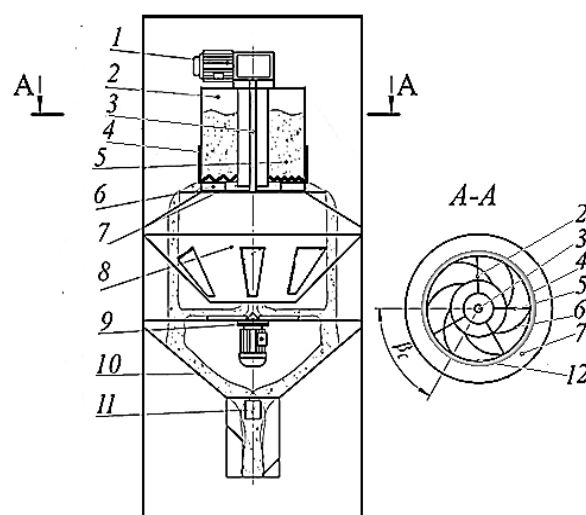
Конструктивно-технологическая схема дозационно-смесительного устройства: 1 — двигатель-редуктор; 2 — подвижная перегородка; 3 — передаточный вал; 4 — подвижная манжета; 5 — неподвижная промежуточная резка; 6 — лопата; 7 — диск; 8 — первая горловина; 9 — разбрасыватель со свободной передачей; 10 — второй горловина; 11 — доски; 12 — бункер
